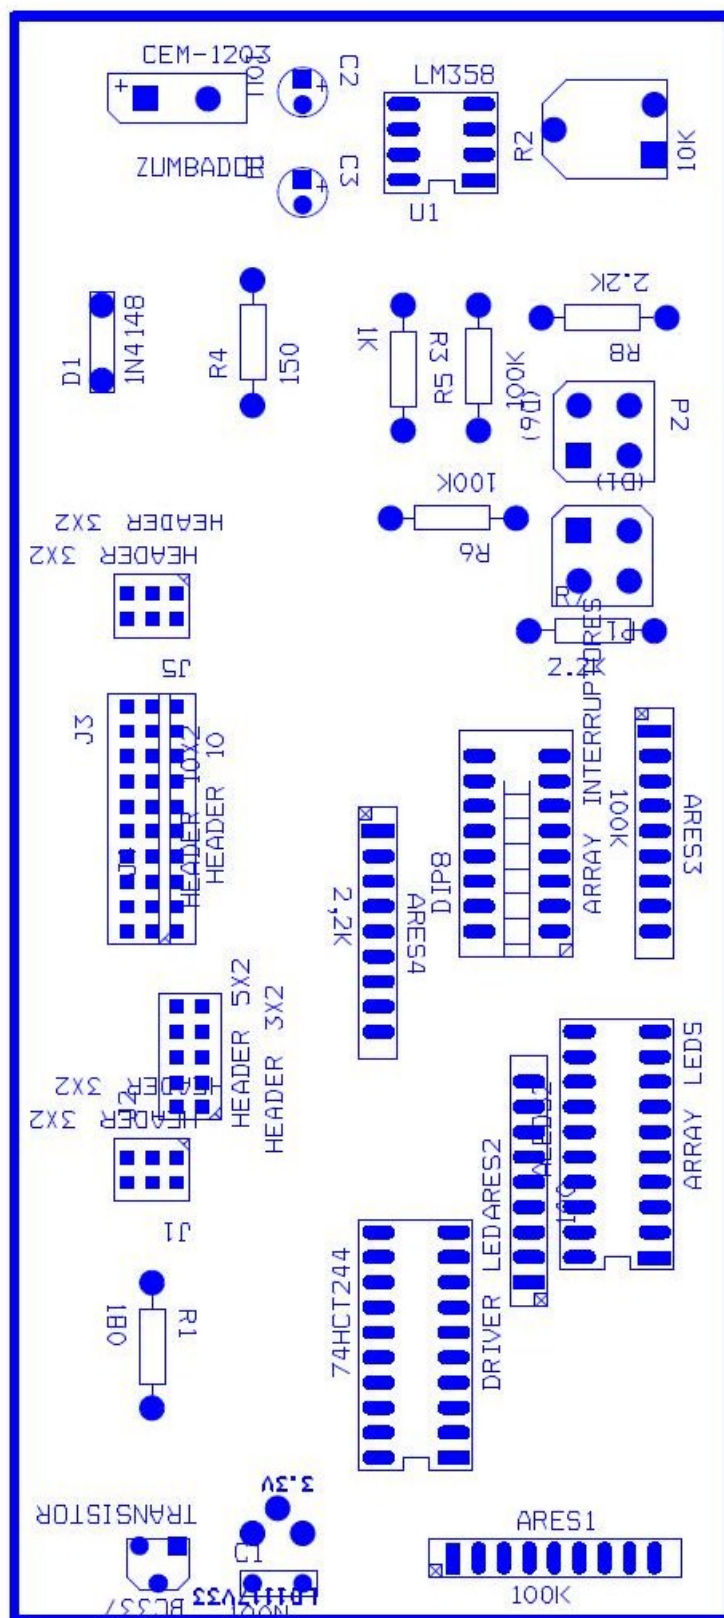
Disposición de los componentes en la cara superior del PCB.
